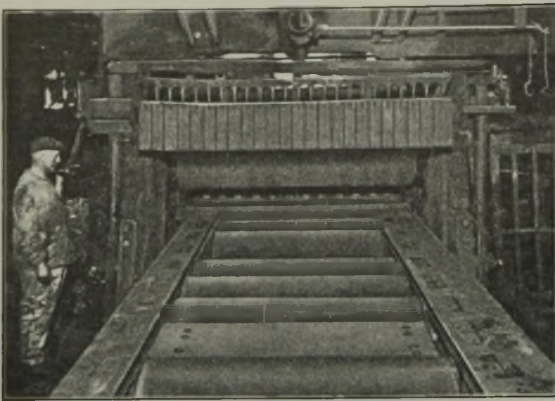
Ansicht der Blechpendel-Schutzvorrichtung.
